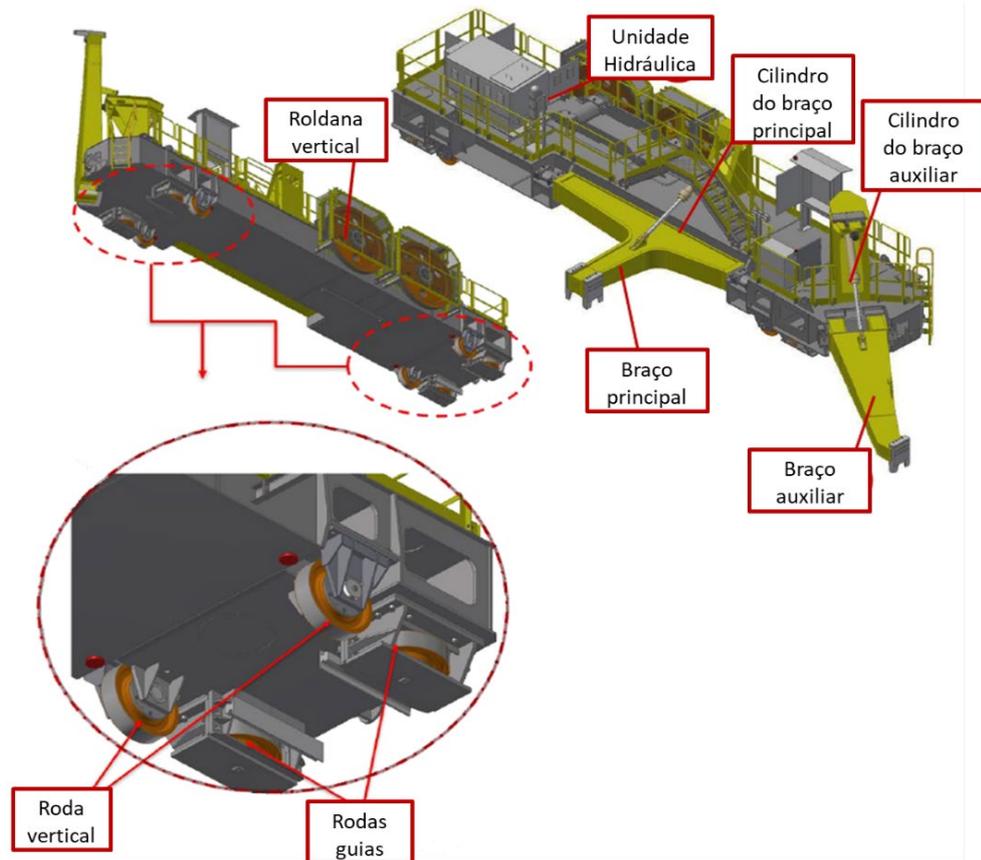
Vista detalhada do carro posicionador com seus componentes (ThyssenKrupp Industrial Solutions, 2003).
